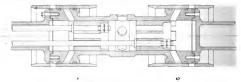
Doppelkolbeusteuerung mit innerem Einlafs, ausgeführt von der Duisburger Maschinenbau-Actiengesellschaft, Duisburg
